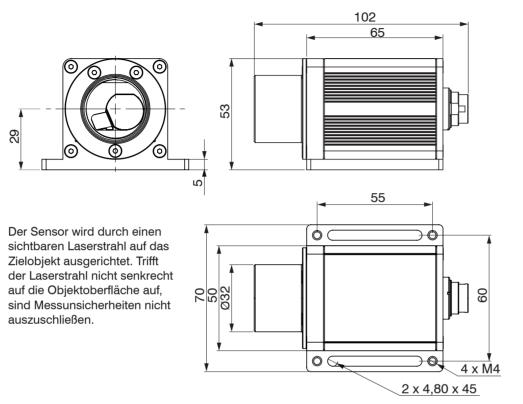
Maßzeichnung optoNCDT ILR2250-100, Abmessungen in mm
